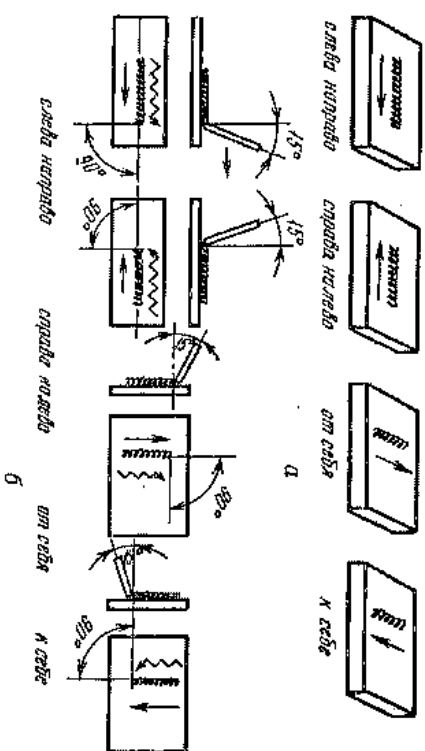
Направления сварки (а) и наклон электрода (б)
